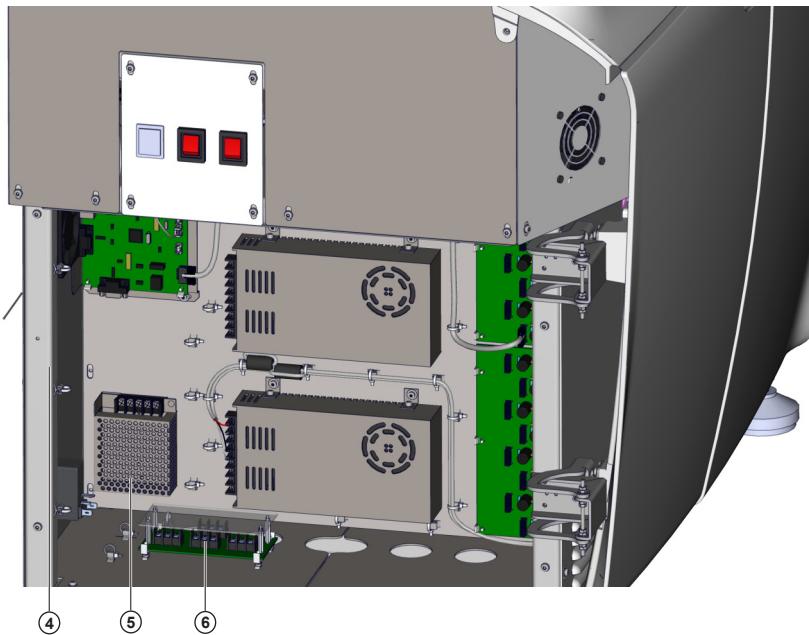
Montaje fuente alimentación módulo ISE
